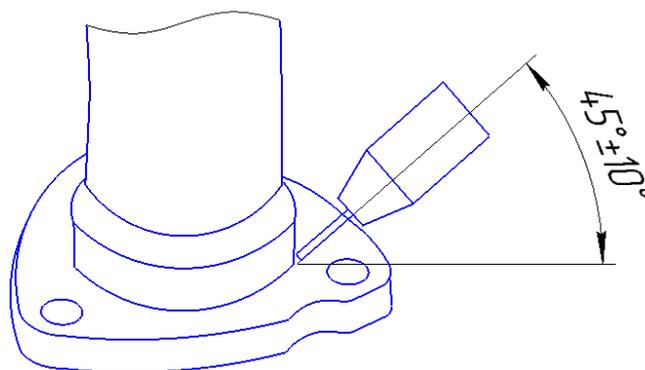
Сварка приемного фланца и трубы передней
